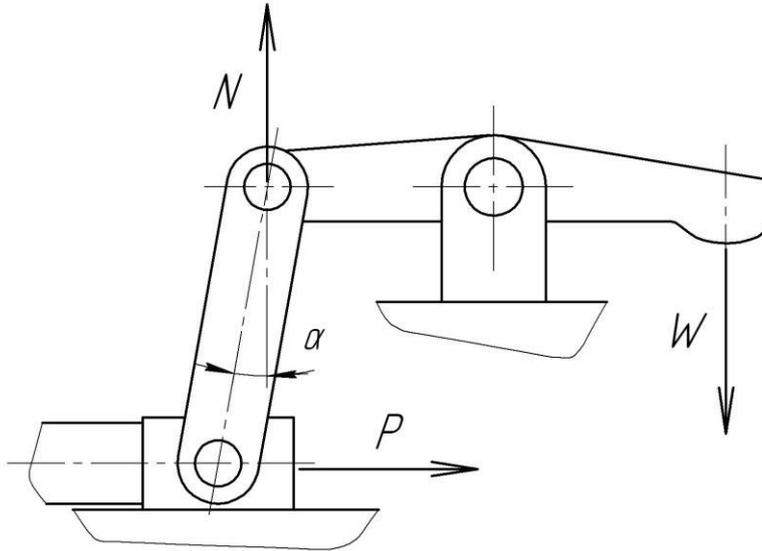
Однорычажный шарнирный зажимной механизм с ползуном
